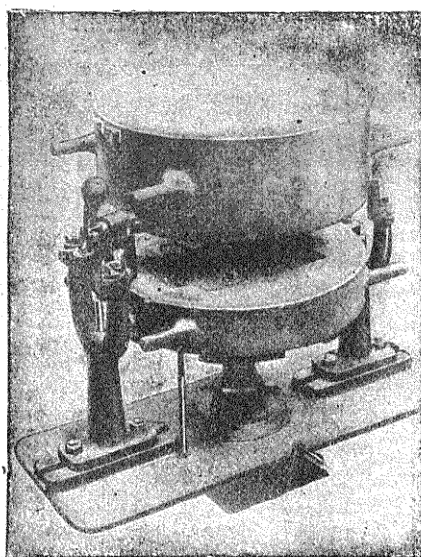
Machine à assembler et à démotter. — Position de démontage.
